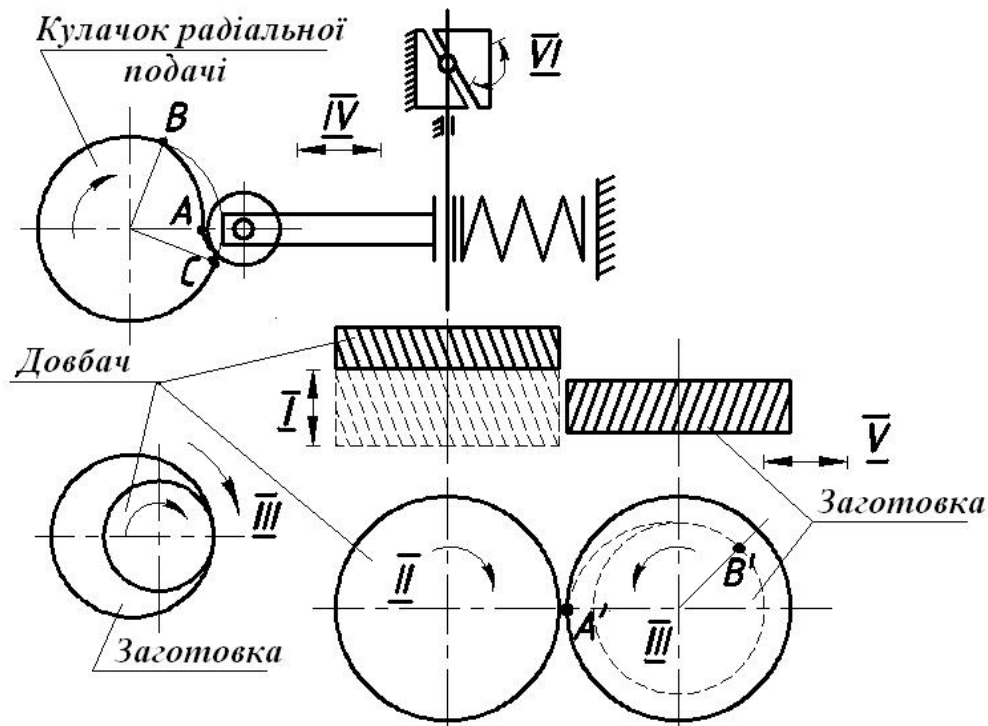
Схема рухів в зубодовбальному верстаті при обробці зубчатих коліс
